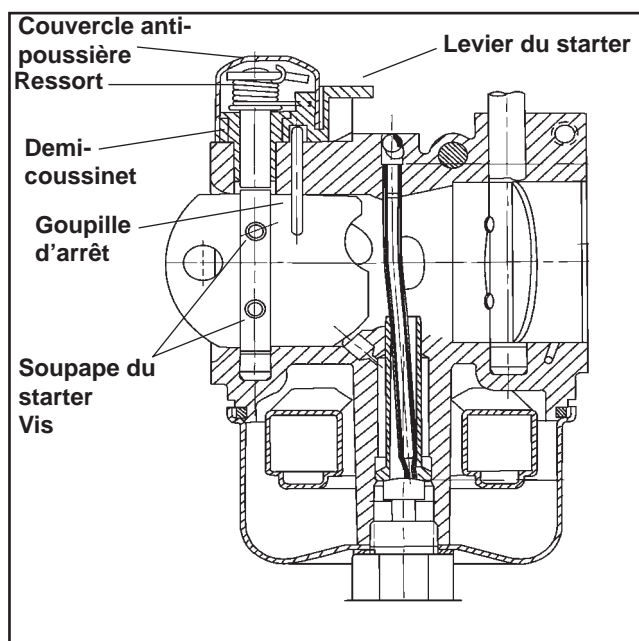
Vue en coupe montrant le carburateur à starter à autodécharge.
